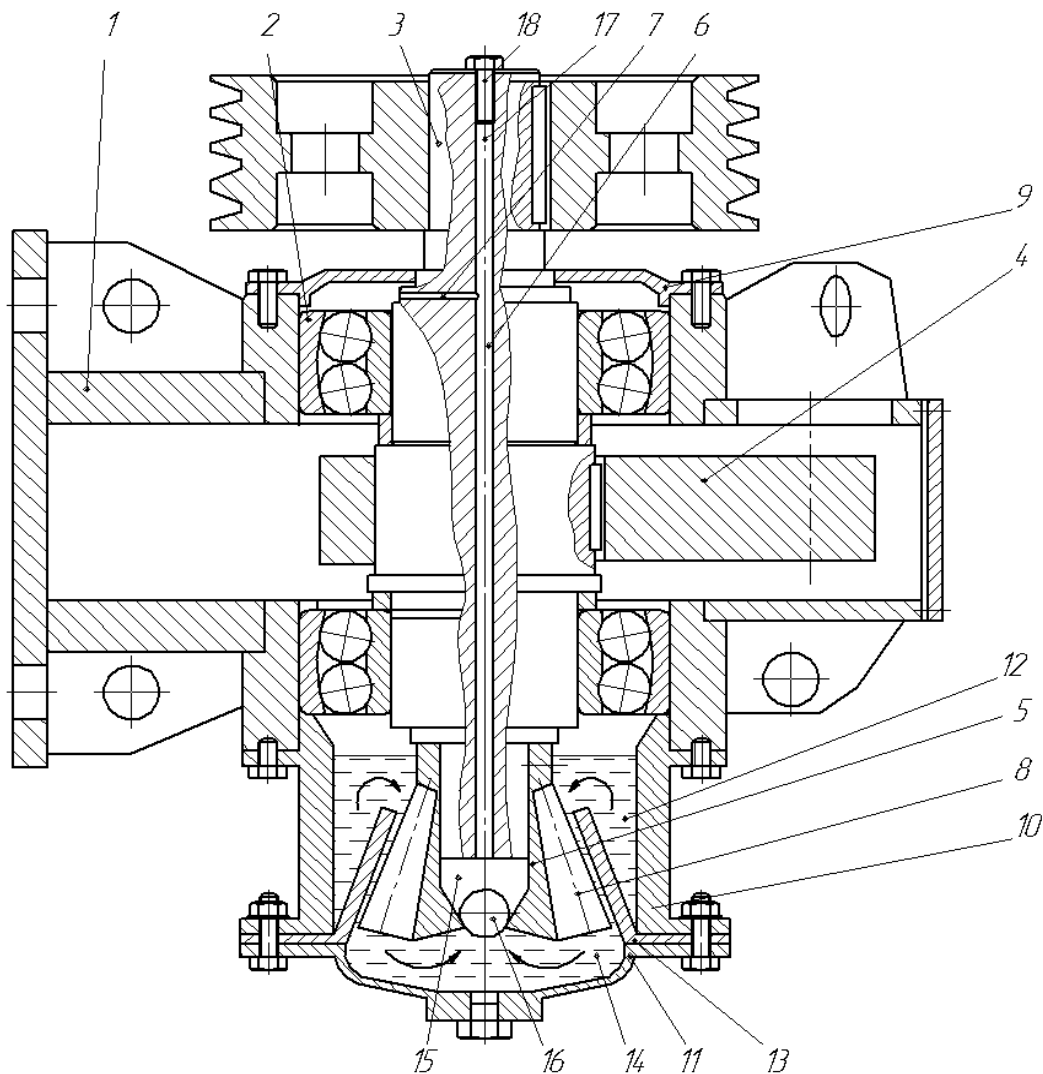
Вібробуджувач з рідинним мащенням підшипників: 1 – корпус вібробуджувача; 2 – підшипник; 3 – вал; 4 – дебаланс; 5 – напірна втулка; 6 – осьовий канал; 7 – радіальний канал; 8 –
